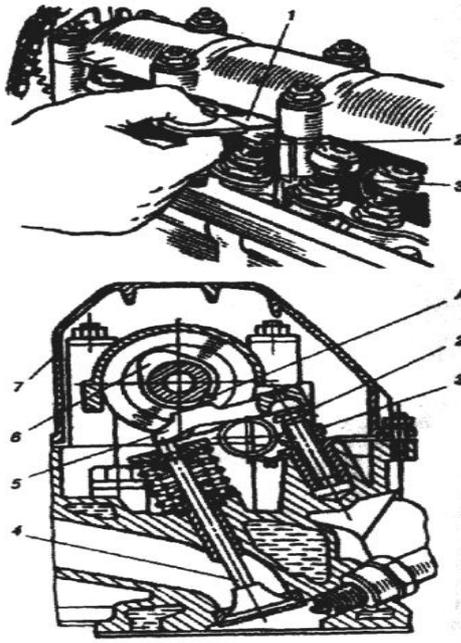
Проверка и регулировка тепловых зазоров в механизме привода клапанов двигателя ВАЗ-2106-70:
